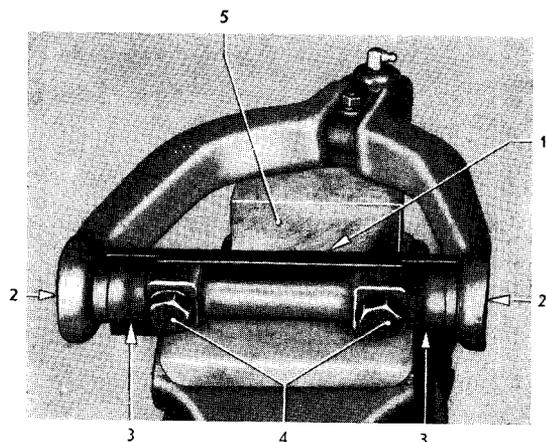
Obere Lenkerachse auf Vorspannstück festschraubt
